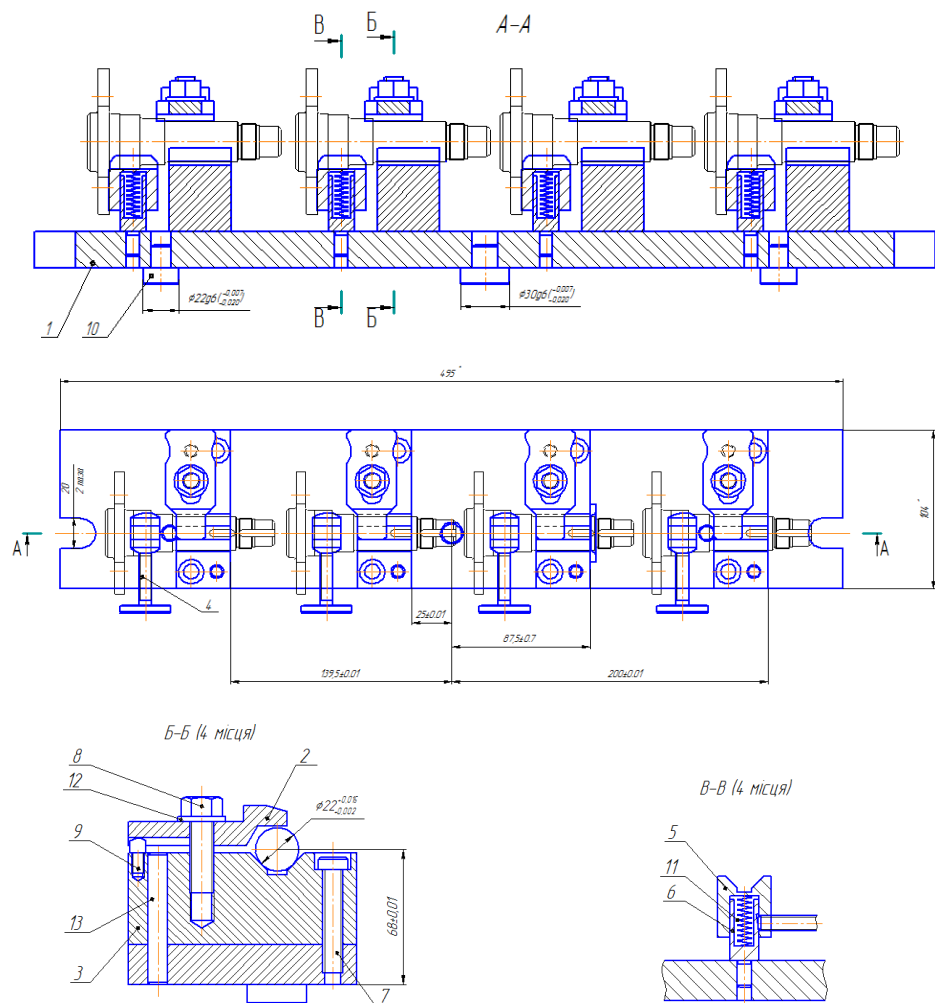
Ескіз пристосування для фрезерування шпонкових пазів
